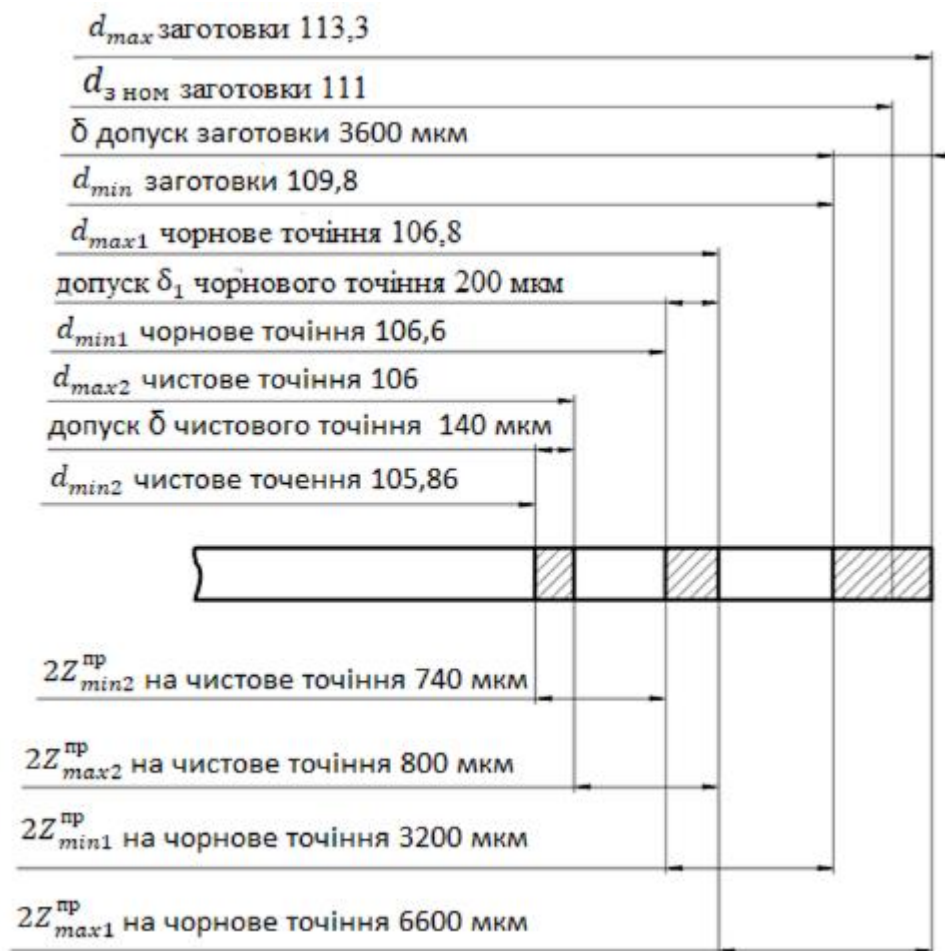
Схема розташування припусків на обробку поверхні $\varnothing 106h10$
